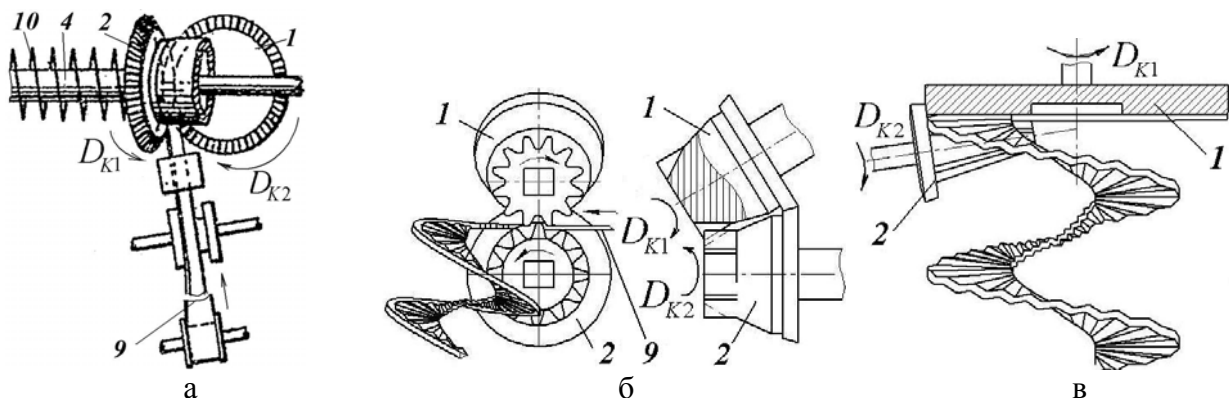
Схеми формоутворення ГГЗ способом асиметричного обтискування гладких смуг між формувальними валками із зубчастими робочими поверхнями:
